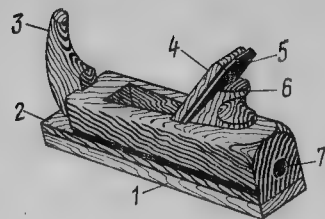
1 — нижняя часть колодки (подошва); 2 — верхняя часть колодки (корпус); 3 — рога; 4 — клин; 5 — нож; 6 — упор; 7 — пробка
